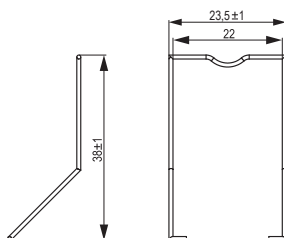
Габаритные и установочные размеры скобы / Figure 8 - Overall and mounting dimensions of the bracket / 8 сурет – Қапсырғыштың габариттік және орнату өлшемдері CRS-M-1
